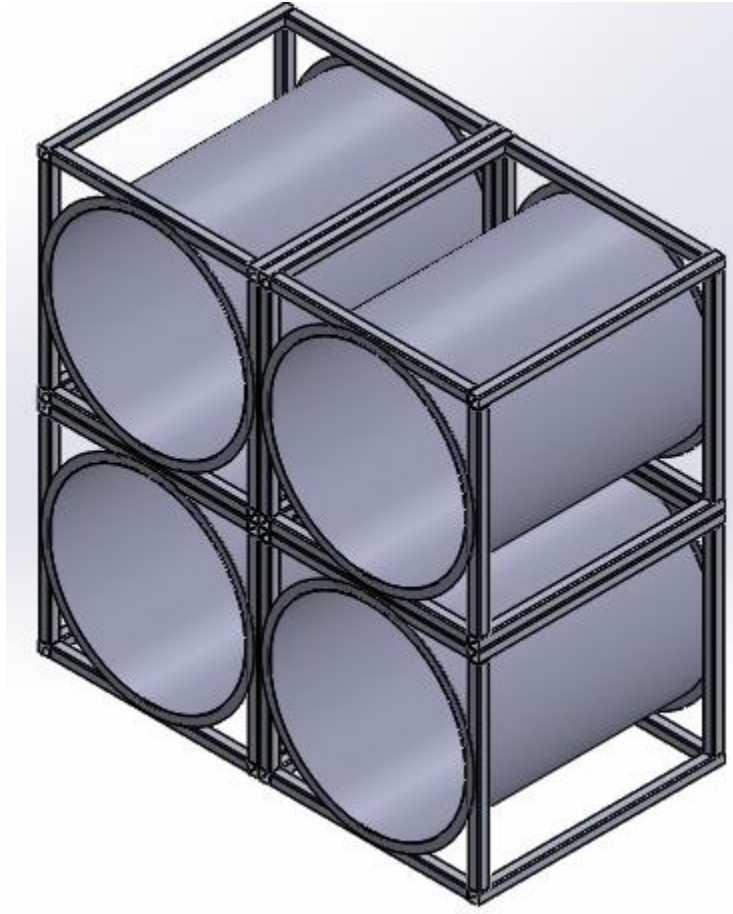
Planta de potencia. Fuente: Generación propia (Solid Works 2018).
